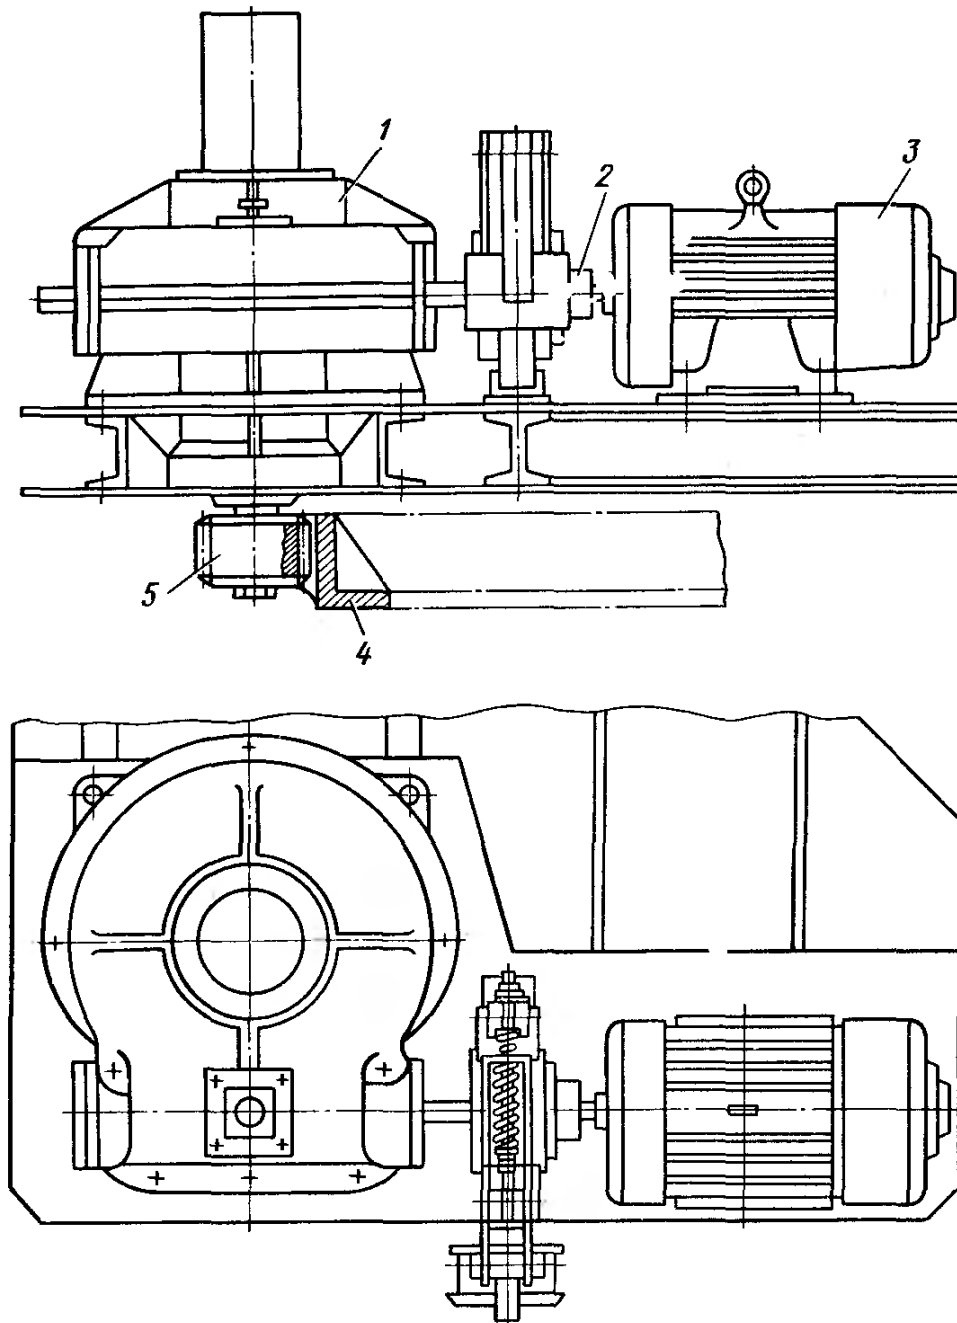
Механізм повороту крана з черв'ячним редуктором
